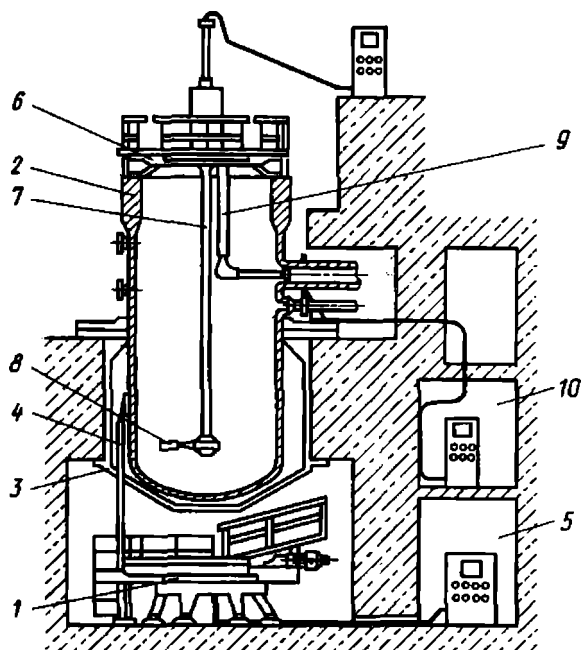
Общая схема контроля корпуса реактора ВВЭР-440
